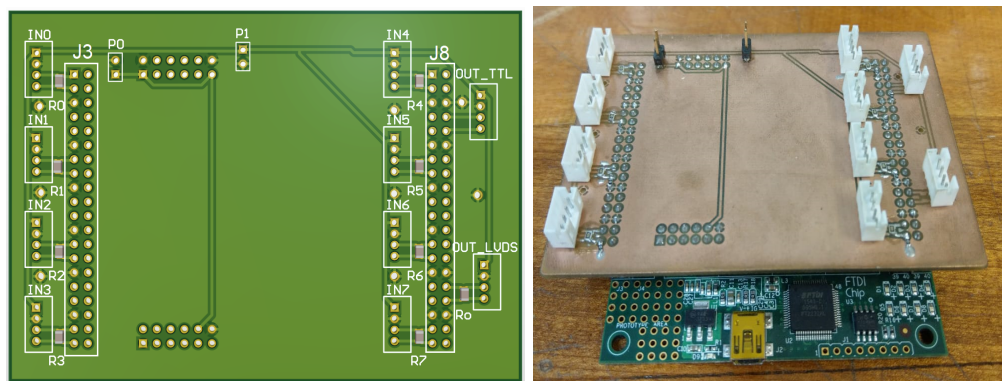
Tarjeta PCB interfaz para la MCU. En la izquierda se muestra el diseño de 3D provisto por el software Altium Designer. En la derecha, la PCB fabricada y montada sobre la CPLD.
